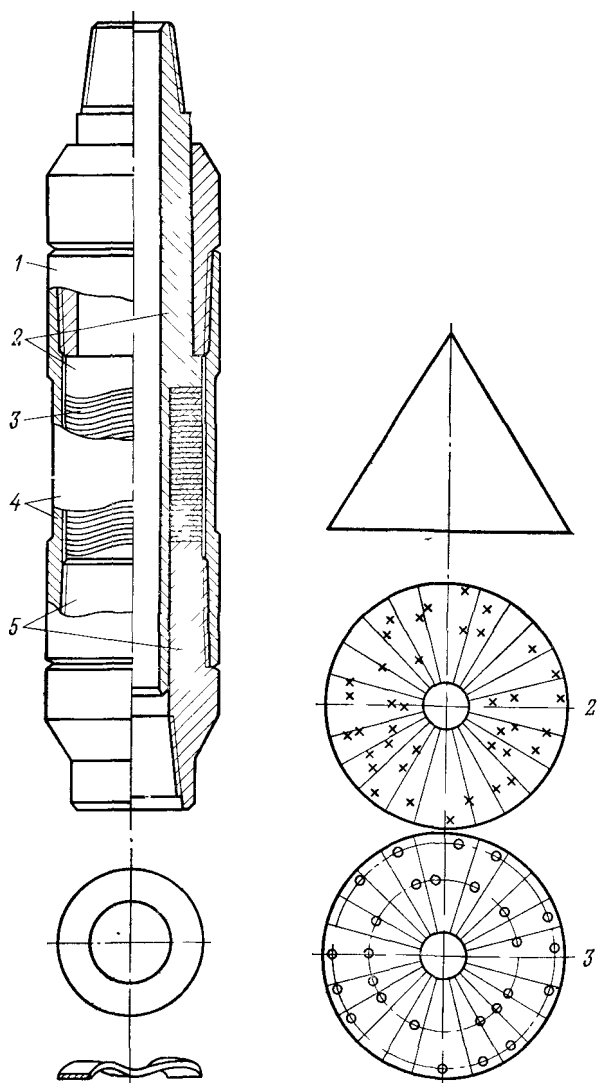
Пластиновый амортизатор, заполненный высоковязкой жидкостью: 1, 5 — верхняя и нижняя муфты, 2 — шток; 3 — рифленные пластины, 4 — корпус
